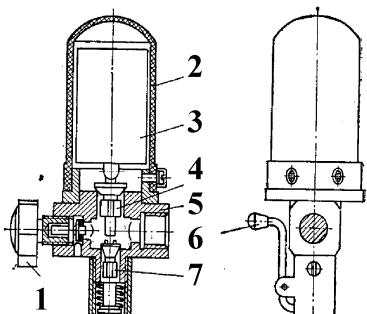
Подвійний запобіжний клапан: 1 – ручка повітряного крану; 2 – кожух; 3 – вантаж; 4 – паровий клапан; 5 – корпус; 6 – важіль підриву вакуумного клапана; 7 – вакуумний клапан
